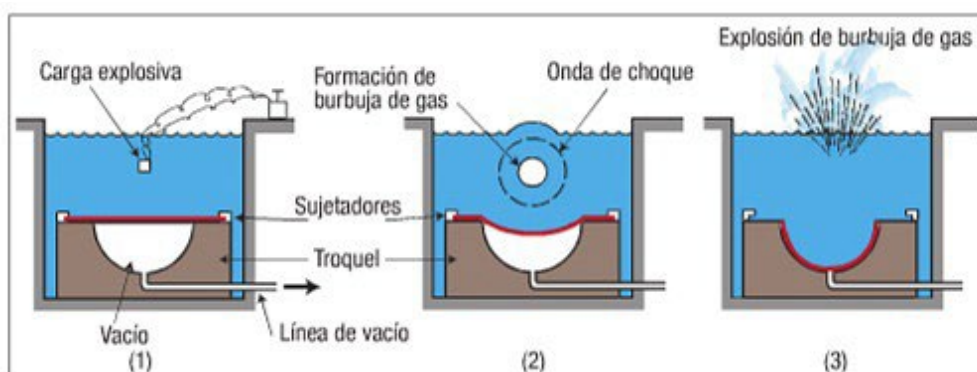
Esquema mostrando el proceso de conformado por explosión. [L-46]
